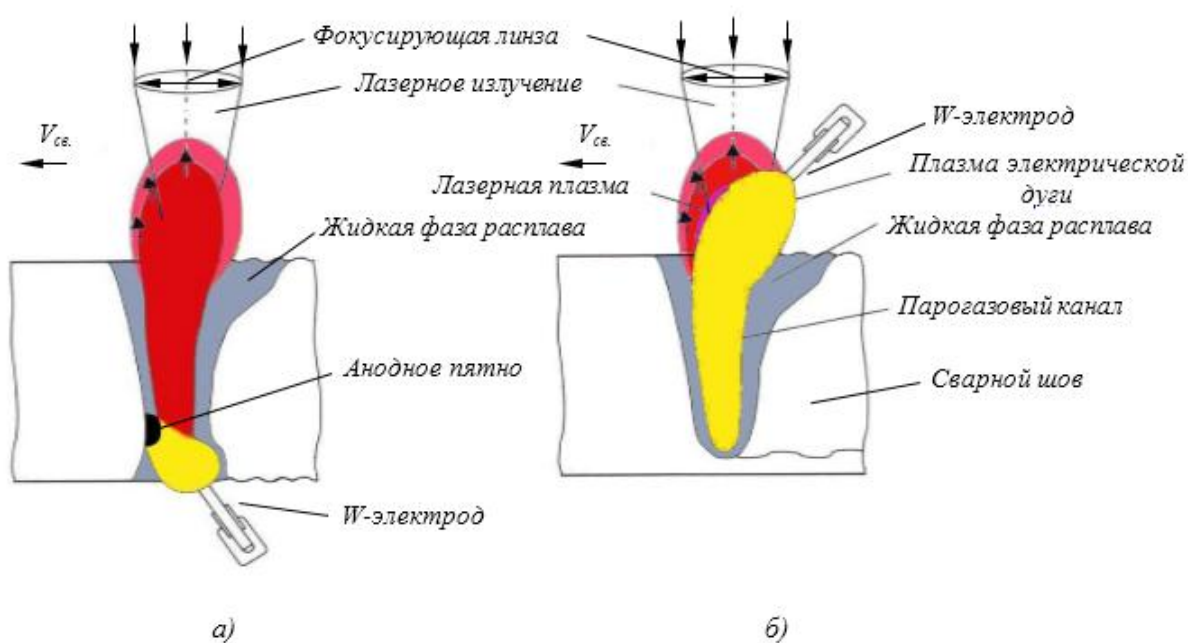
Геометрические схемы реализации процесса лазерно-дуговой сварки [12].
